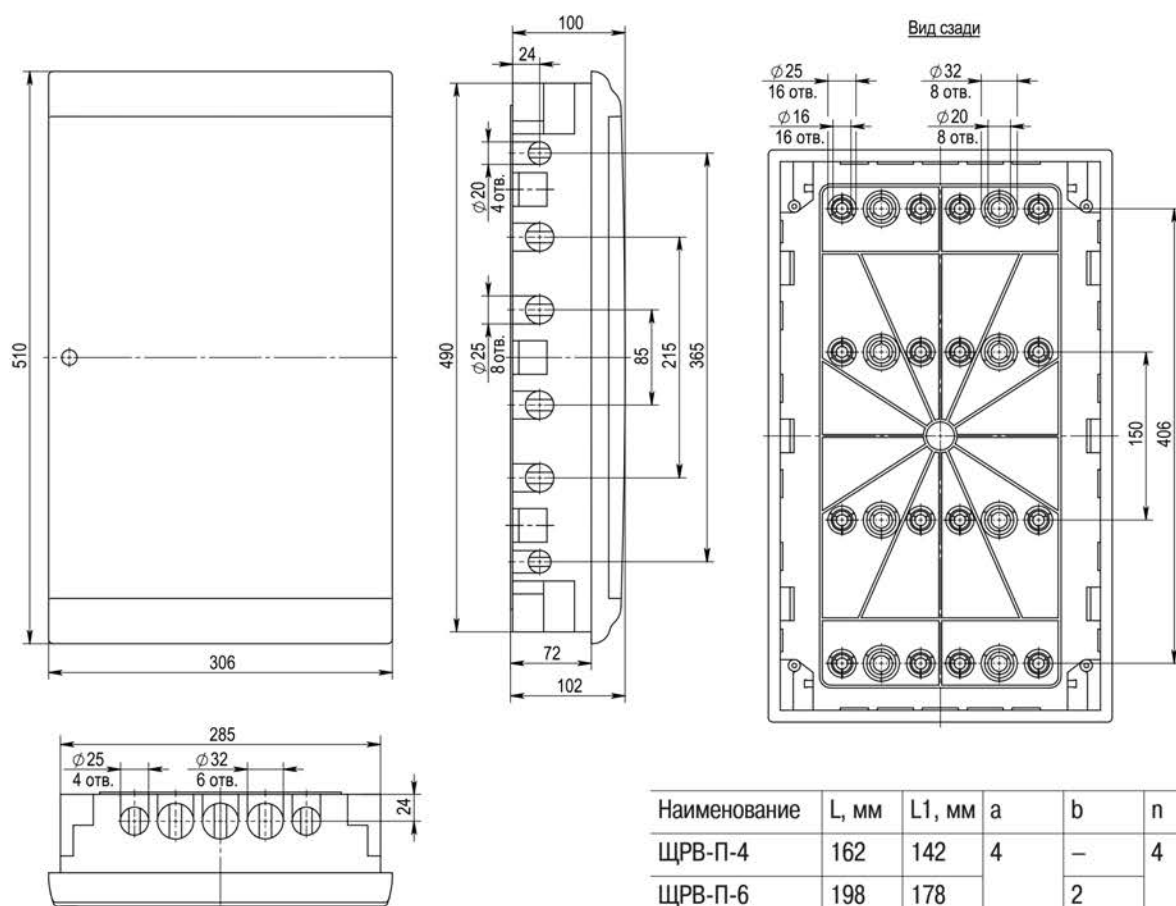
Габаритные и установочные размеры корпуса ЩРВ-П
